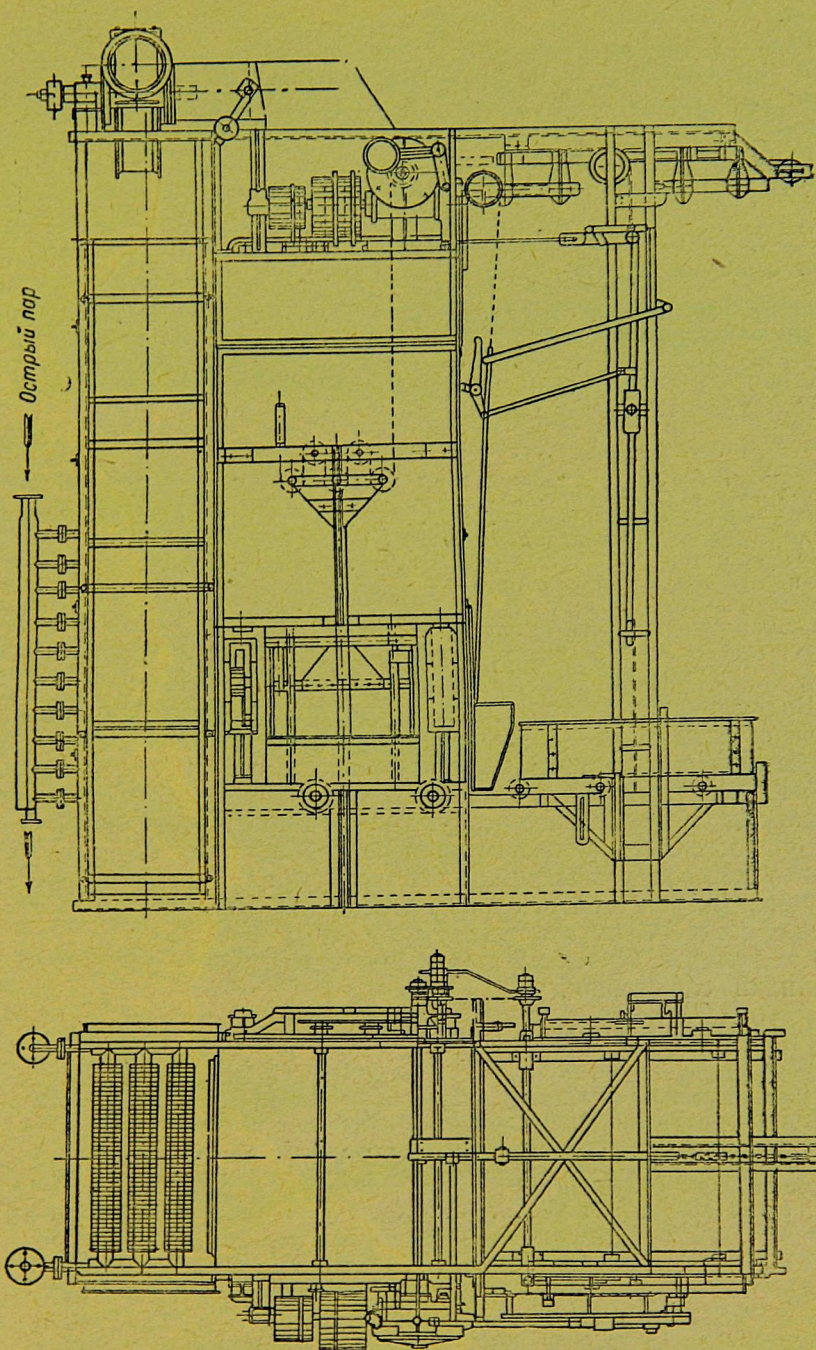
Сушильный шкаф США (вид сбоку и план)
